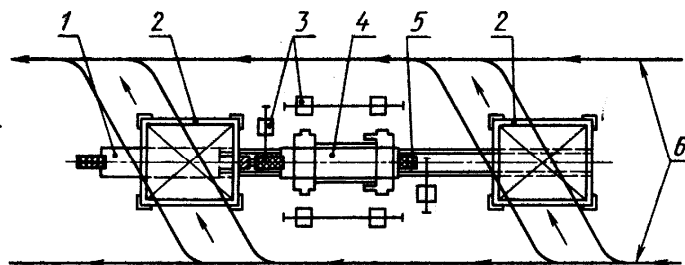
Схема расположения главного кондуктора для сборки кузовов автомобилей ВАЗ
